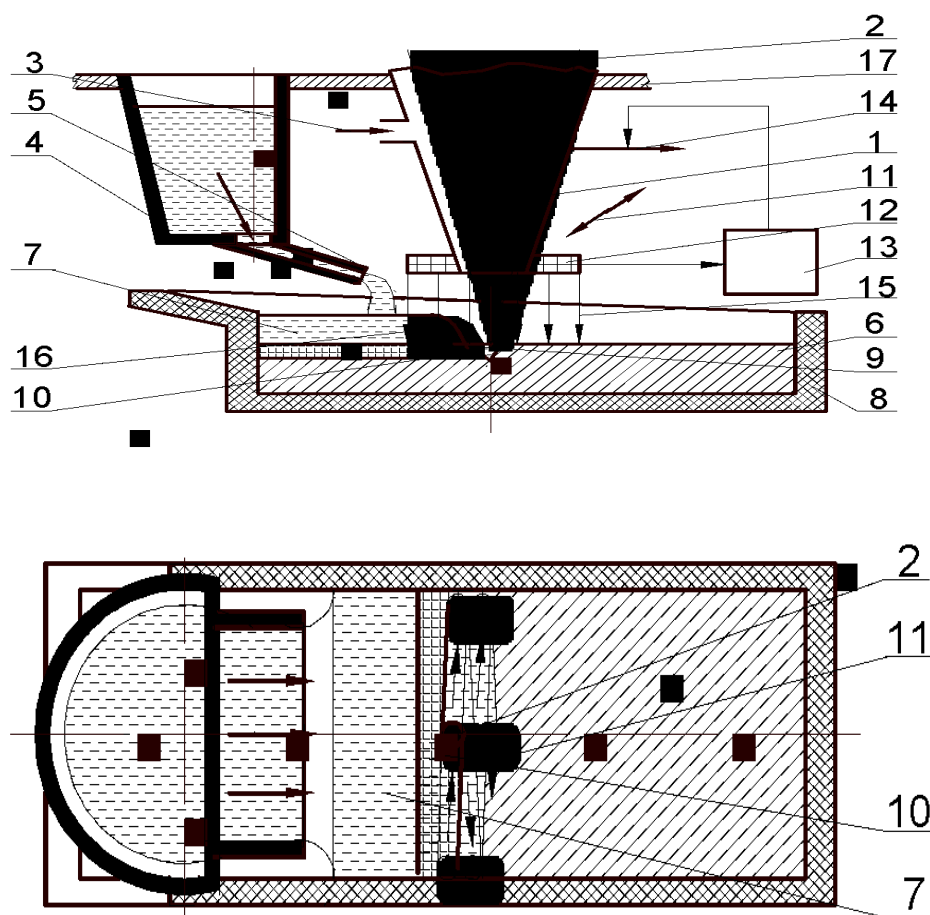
Пристрій для автоматизованого лазерно-ливарного виготовлення біметалів
